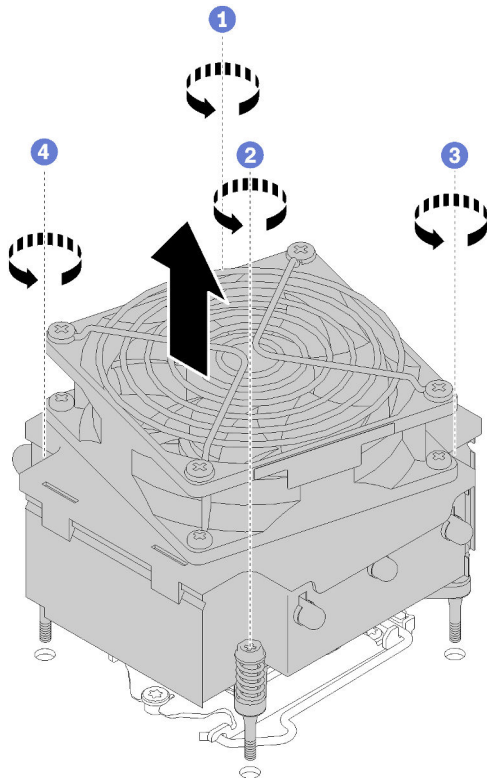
Retirer le dissipateur thermique et du module ventilateur
